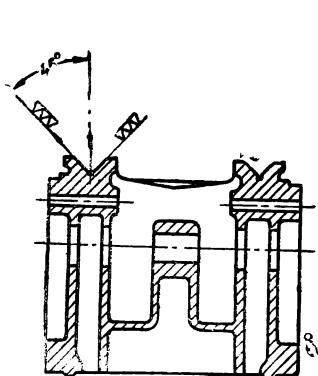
Форма направляющих станины токарных станков типа Дип-20.
